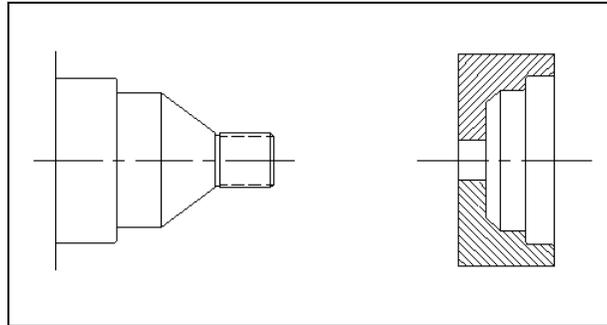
Pieza para Mecanizar en Centro de Maquinado
